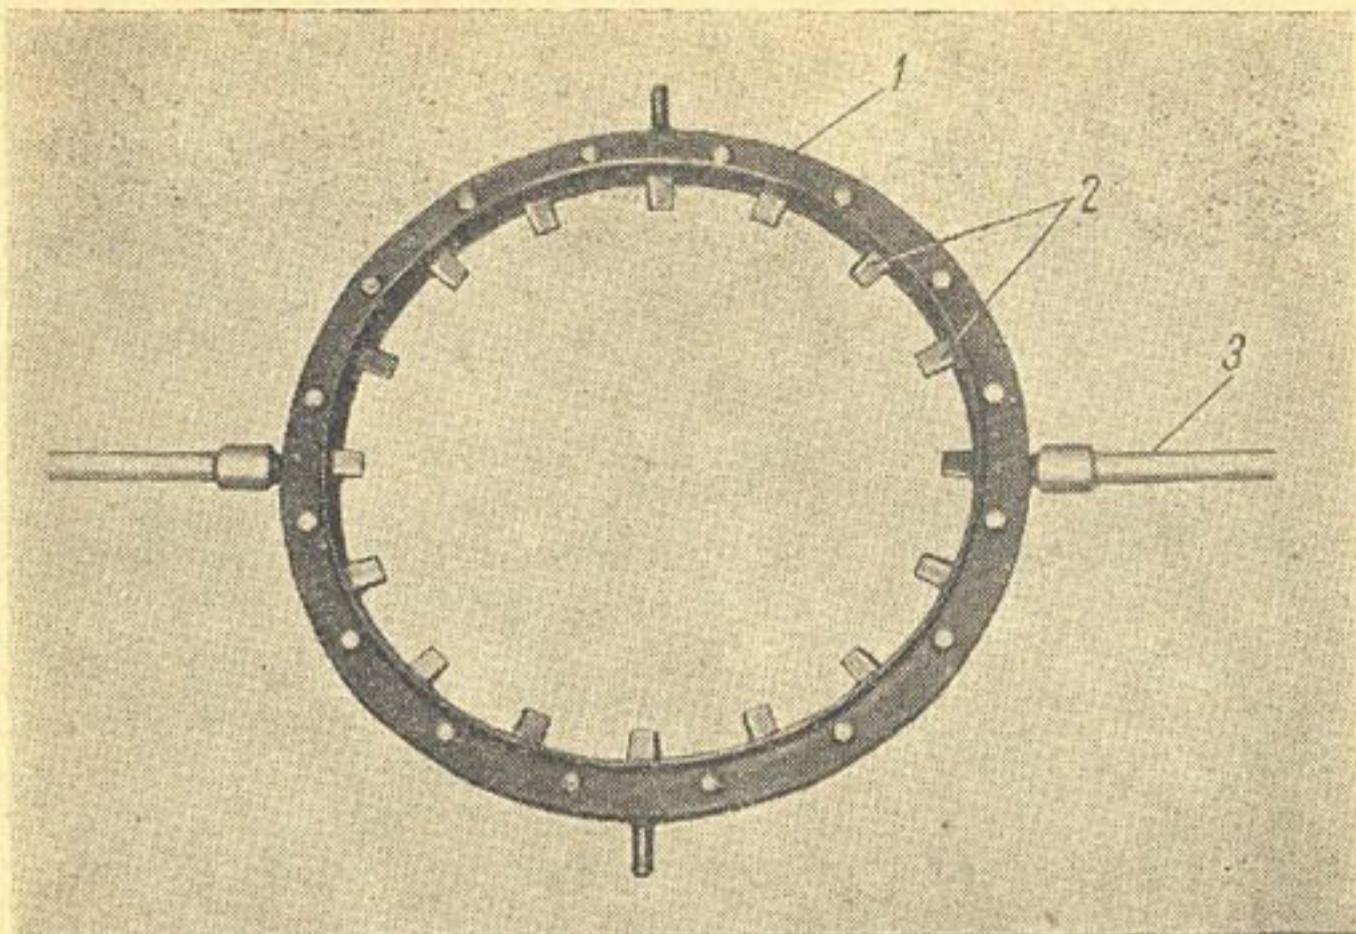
Ручная фреза для торцовых труб из пластмасс:
